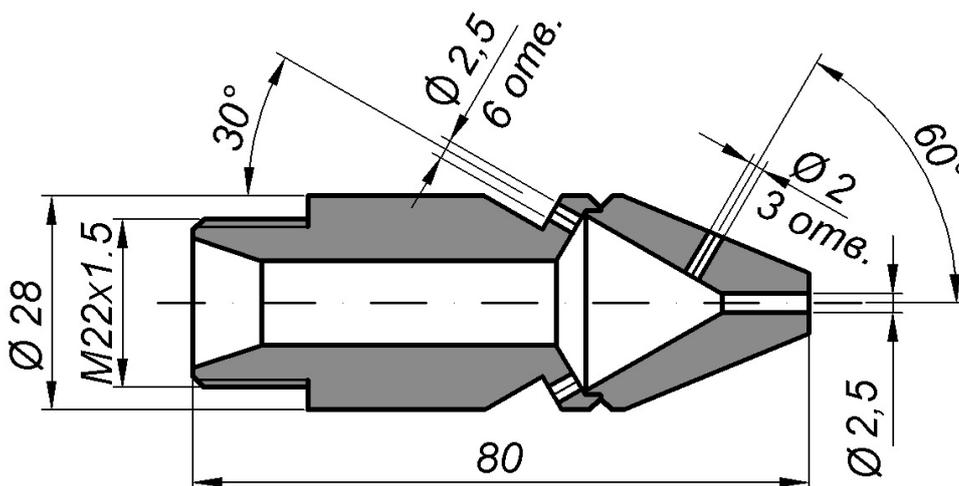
Конструкция промывочной насадки, применяемой в устройстве промывки дренажа УПД-120
